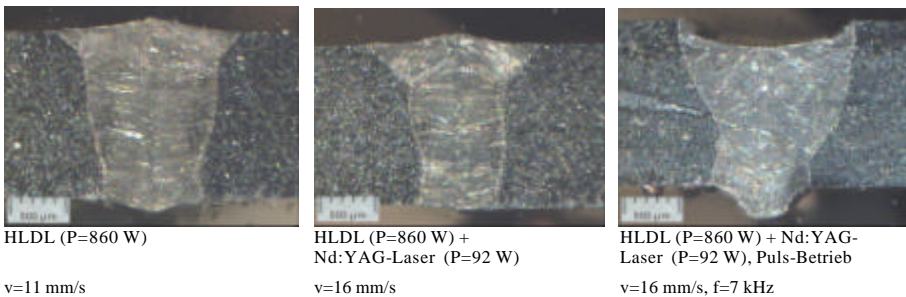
Nahtquerschnitte von Stumpfstoßschweißungen mit Edelstahl 1.4301 (Dicke 1,5 mm)
